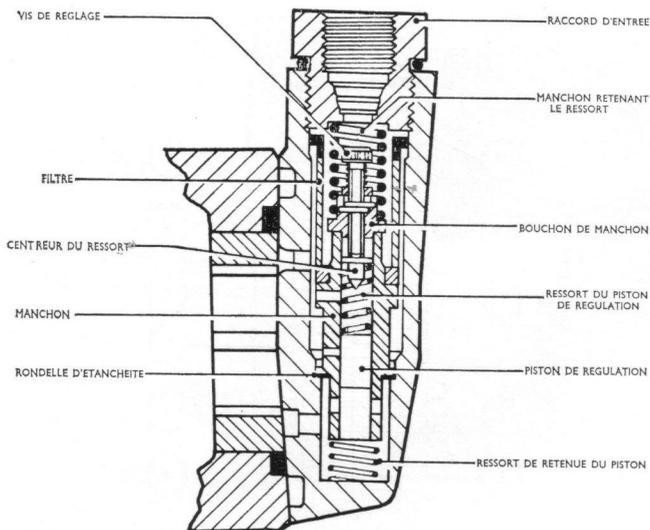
Couvercle équipé d'une vis de réglage de pression de transfert
